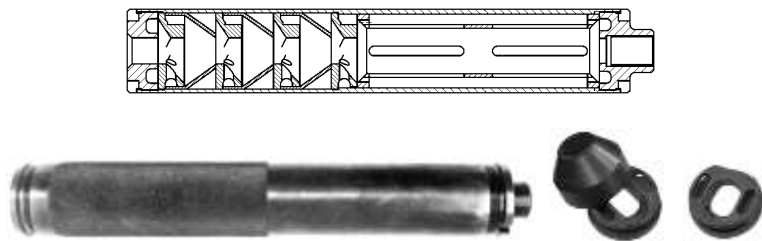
Конструктивная схема и внешний вид ПСУЗВ-150-9,0
